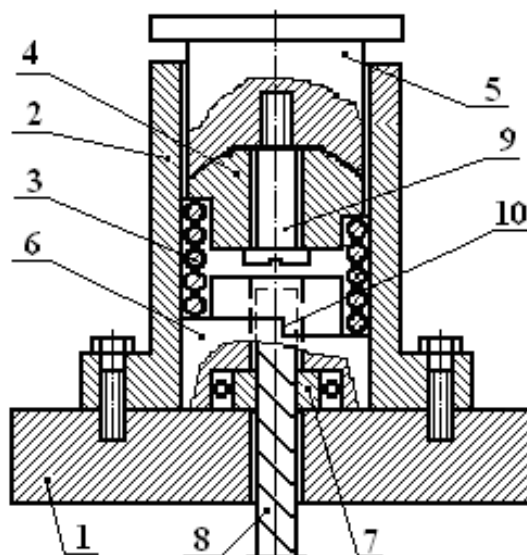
Устройство для заневоливания пружин по пат. RU 2286556 [98]
